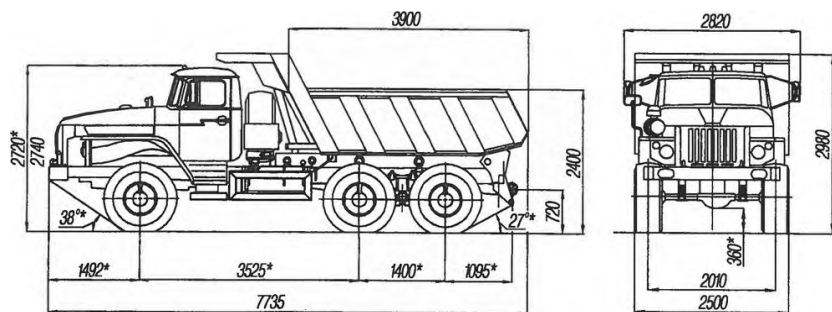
Габаритные размеры автомобиля-самосвала Урал-55571-40.
